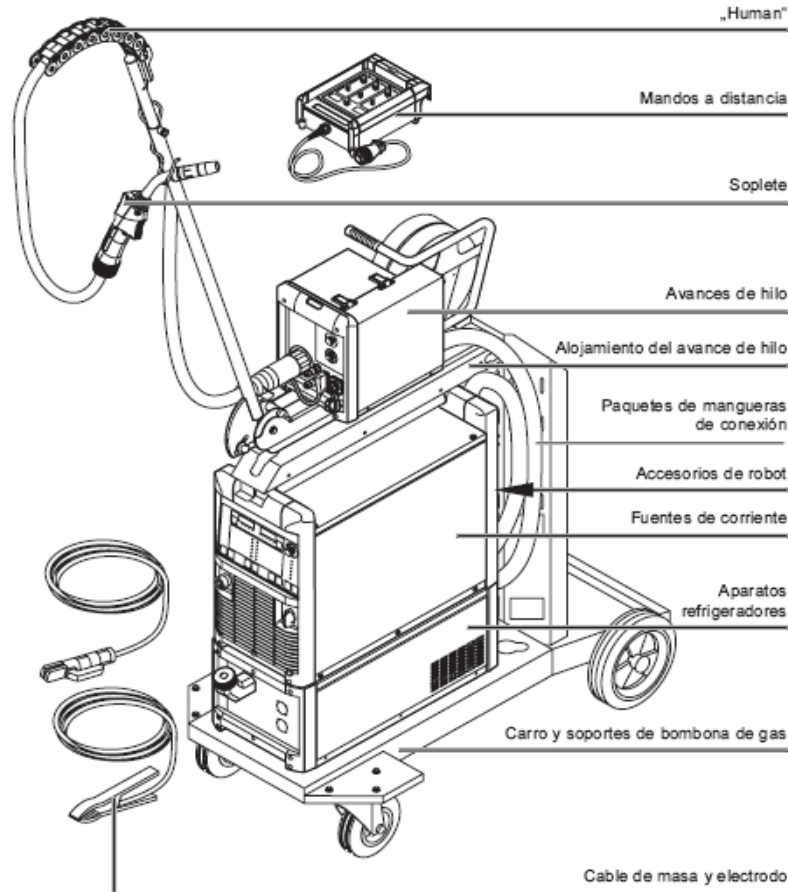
Equipo completo de soldadura al arco FRONIUS
